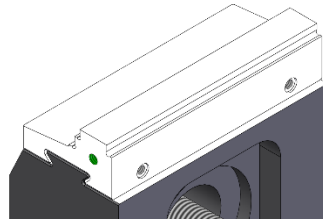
Spannbacke mit glatter Stufe Detailansicht
